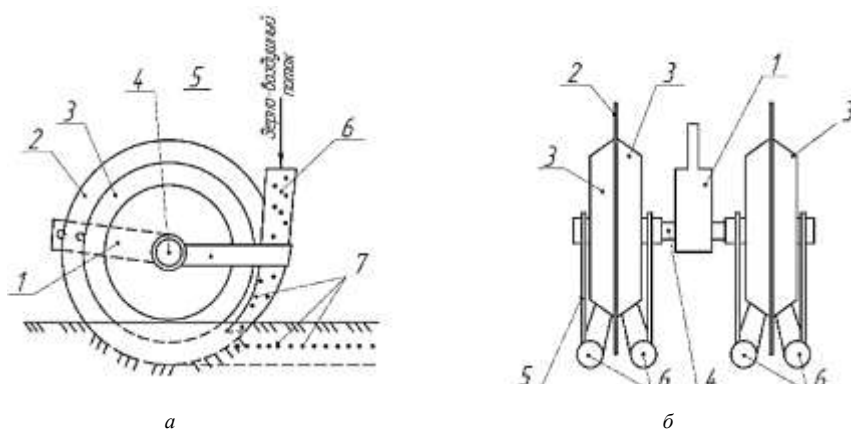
Технологическая схема работы двухдискового четырехстрочного сошника с усеченно-конусными ребордами и нулевым углом атаки дисков: *а* – вид сбоку; *б* – вид сверху; 1 – корпус; 2 – диск; 3 – реборда; 4 – ось; 5 – пластина; 6 – семянаправители; 7 – семена
